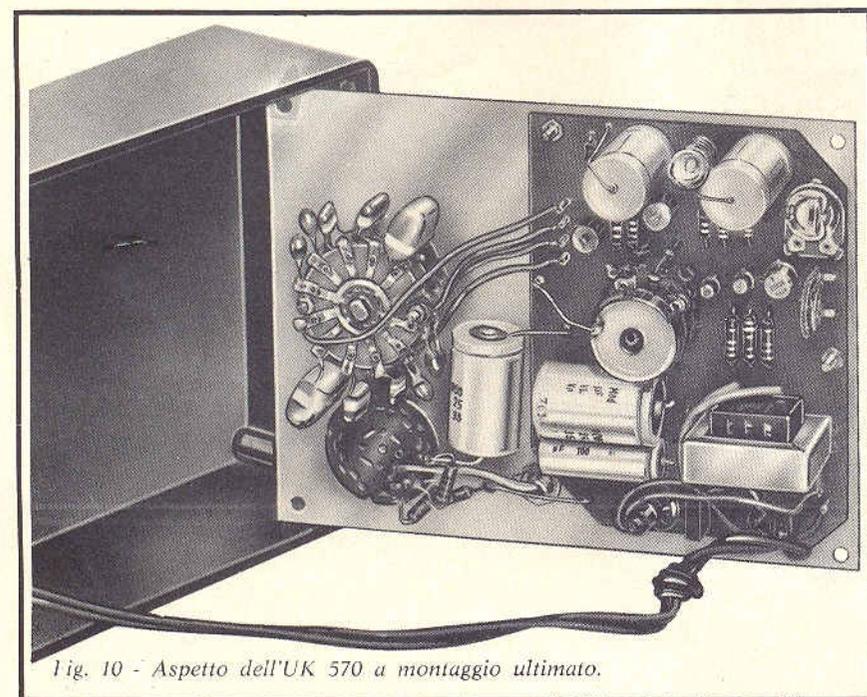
Aspetto dell'UK 570 a montaggio ultimato.
